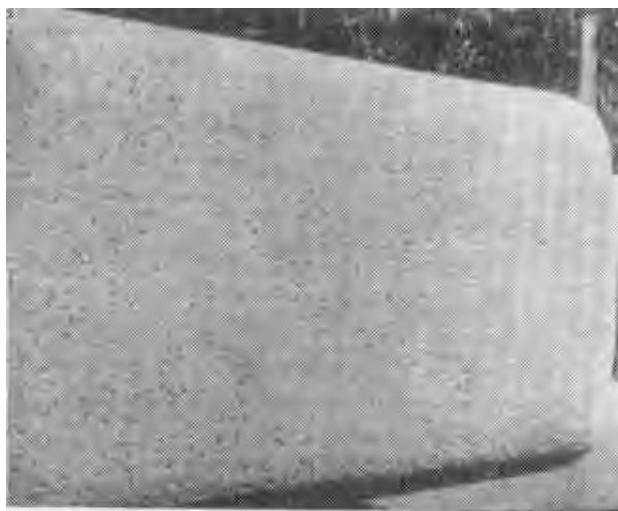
Пузыри на поверхности слитка спокойной стали
